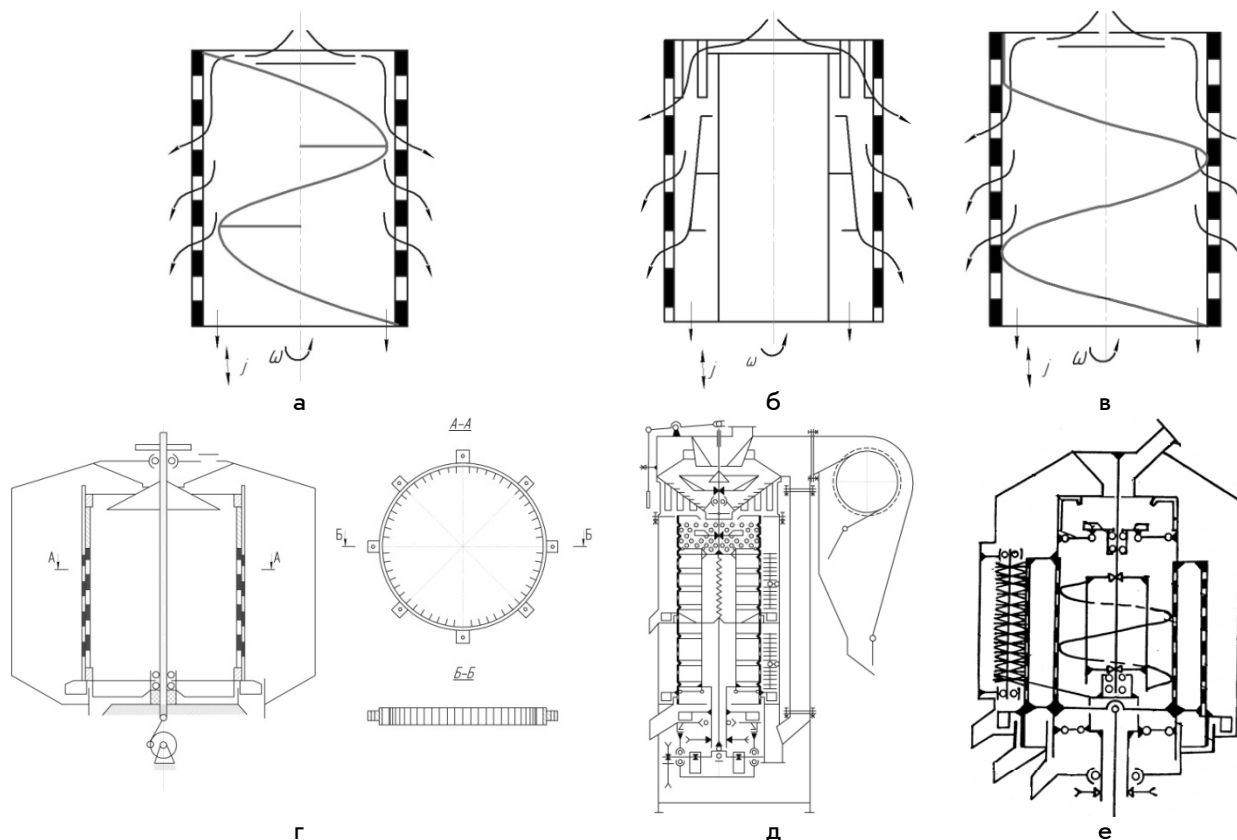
Устройства для стабилизации зернового материала в верхней части цилиндрического решета
